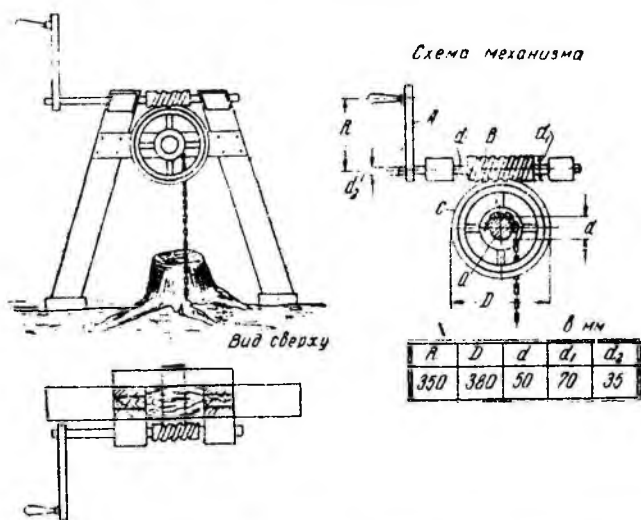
Корчевальная машина Шустера: А — рукоятки; В — червяк; С — зубчатка; О — рабочий вал
